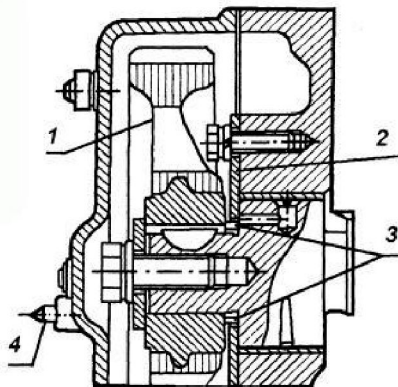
Привод распределительного вала: 1 – шестерня; 2 – упорный фланец; 3 – распорная втулка; 4 – установочный штифт на крышке распределительных шестерен.
